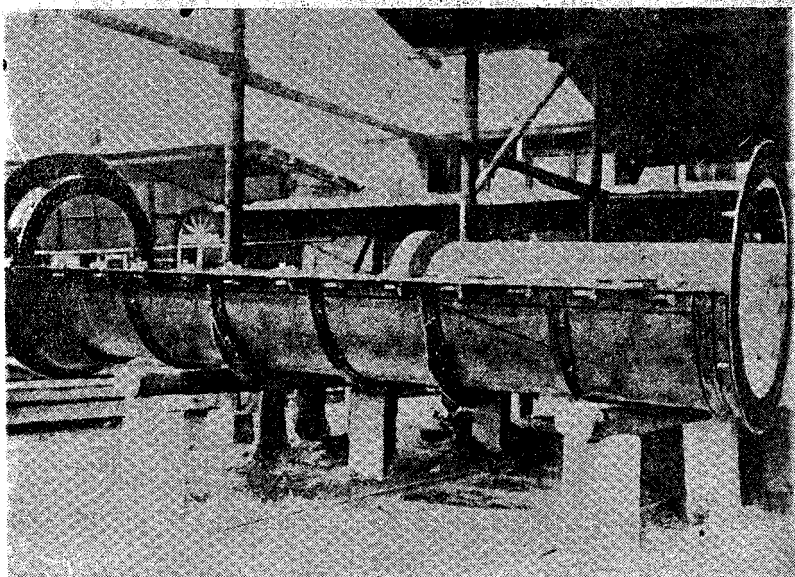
Molde abierto para tubos de 0,800 m. de diámetro el extremo izquierdo está munito de un dispositivo para formar el enchufe.
